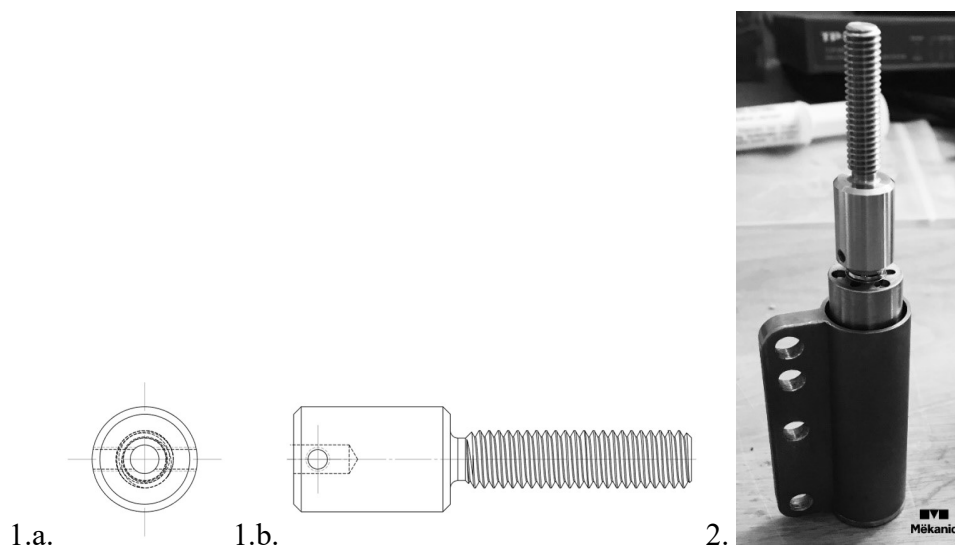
Bloc monolithique englobant l'accouplement mécanique et la tige filetée : 1. Dessins techniques a. vue de gauche et b. vue de face, 2. Photographie du sous-assemblage comprenant le canon et son bouchon puis toutes les pièces standards dont le nouveau bloc monolithique remplaçant l'accouplement mécanique flexible et la tige filetée. ©2020 par Mëkanic. Reproduit avec permission.
